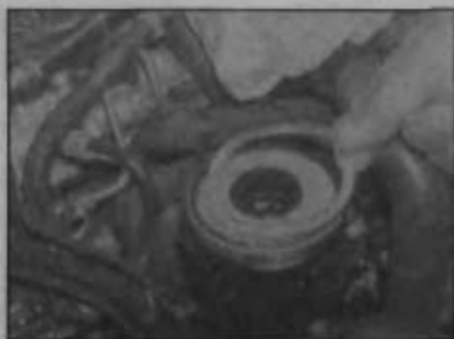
Снятие металлического уплотнительного кольца топливного фильтра
